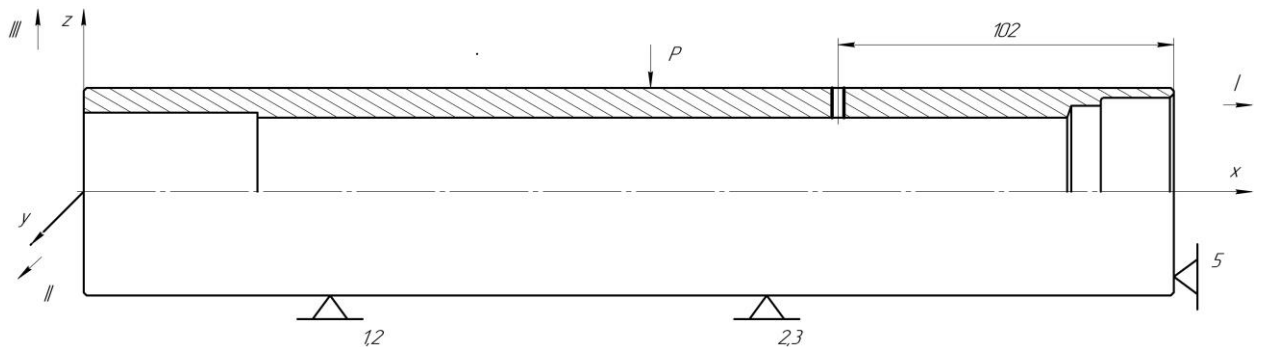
Схема базування деталі в пристрої спеціальному.
